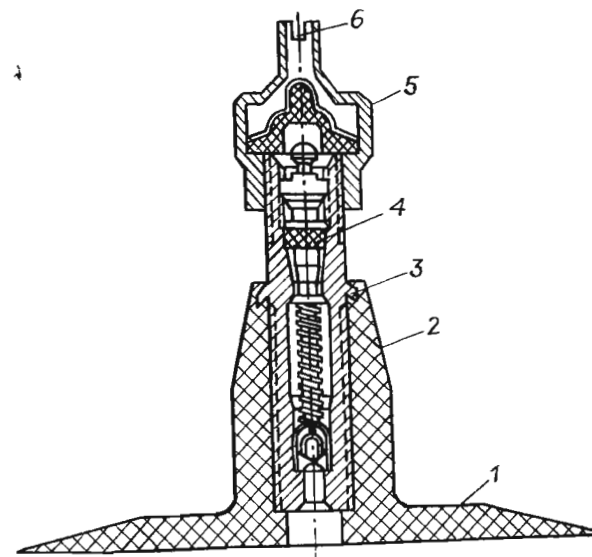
Поперечный разрез резинометаллического вентиля для камер легковых шин:
